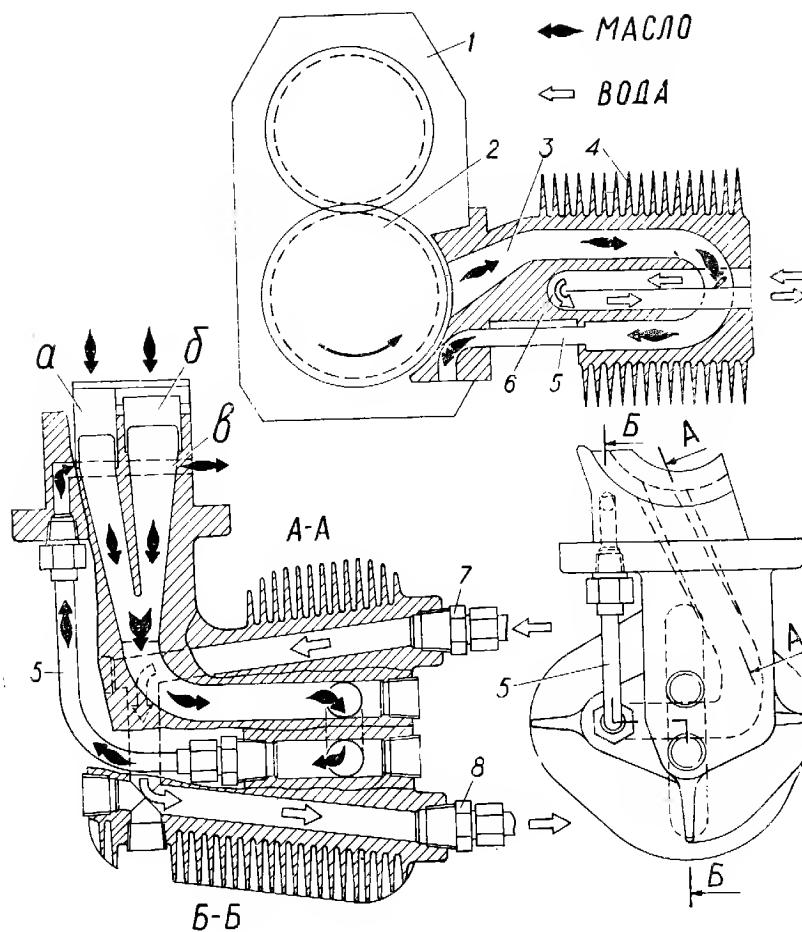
Схема работы маслоохладителя коробки передач:
